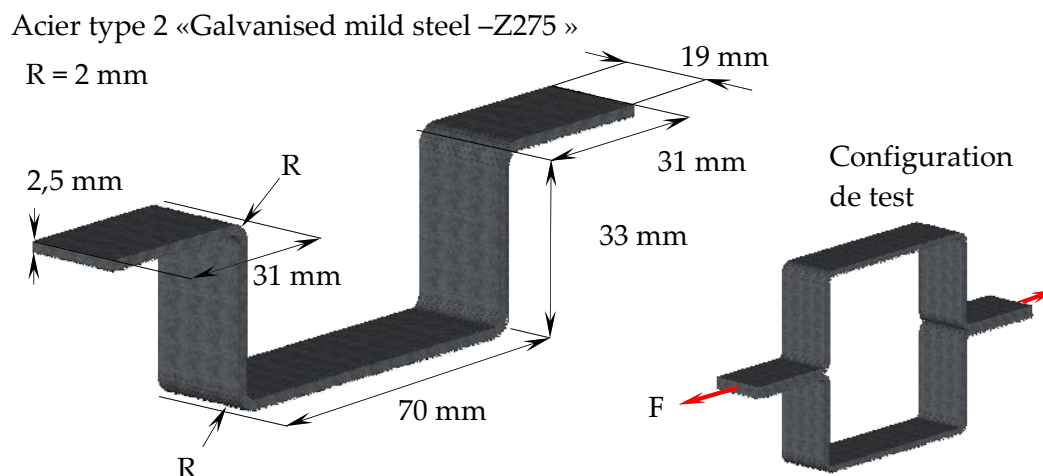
Dimensions des éprouvettes pour l'essai de dépliage.
